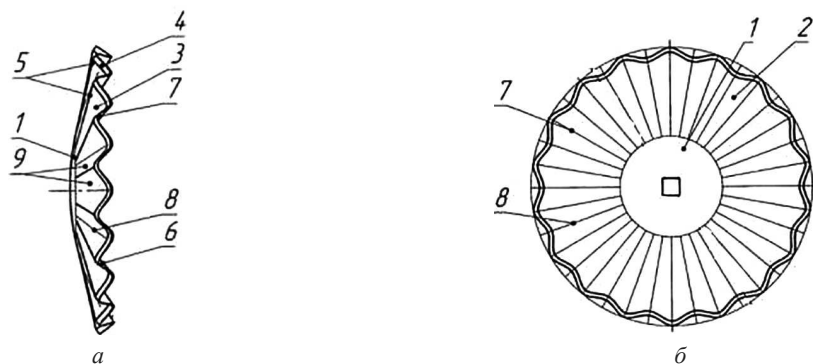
Схема почвообрабатывающего диска: а – вид спереди; б – вид сбоку; 1 – сферическая центральная часть; 2 – наружное кольцо; 3 – гофра; 4 – лезвие диска; 5, 6 – линия гребней; 7, 8 – линия впадины; 9 – боковая поверхность гофры
